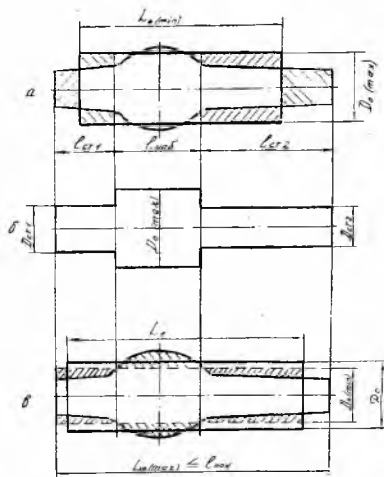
К выбору исходной цилиндрической заготовки для профилирования
